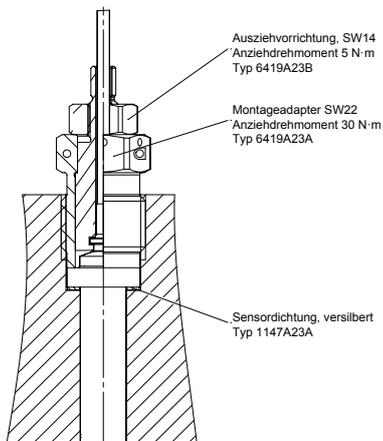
Sensormontage direkt, mit Ausziehvorrichtung Typ 6419A23B
